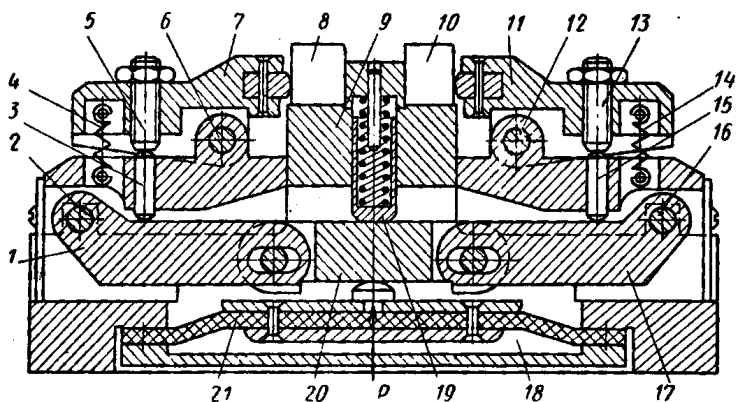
Специальное двухместное приспособление для призматических заготовок:
